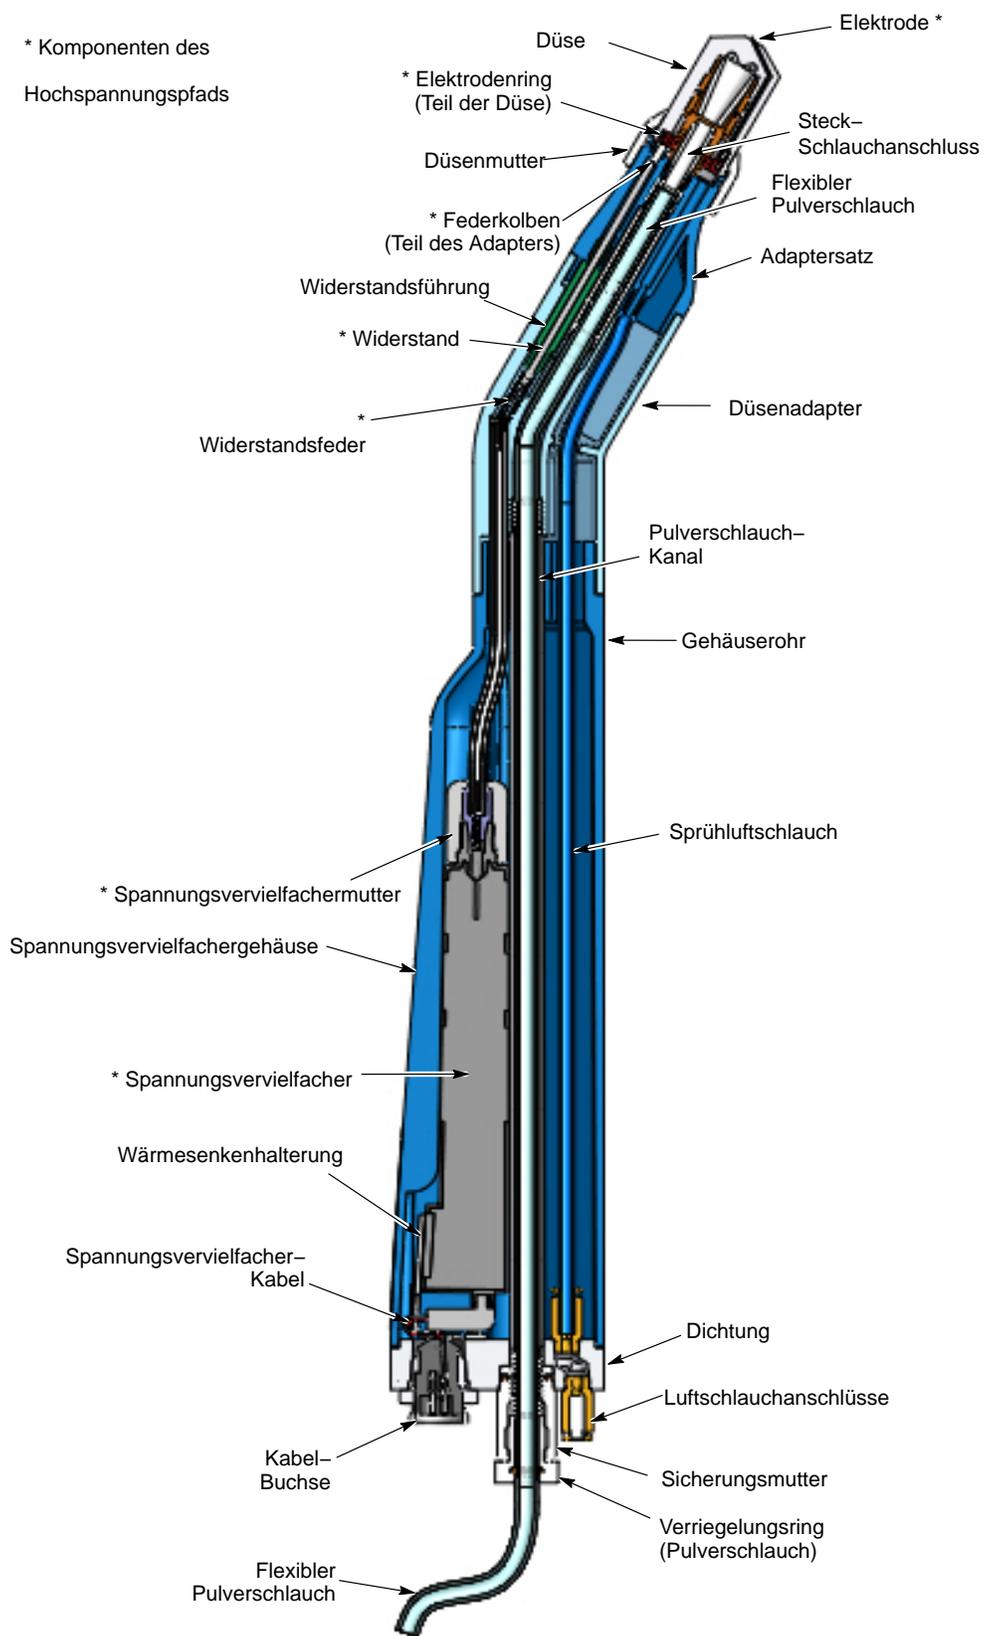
Schnitzzeichnung – Prodigy Robotersprühpistole (mit 30 Grad Düsenadapter abgebildet)
